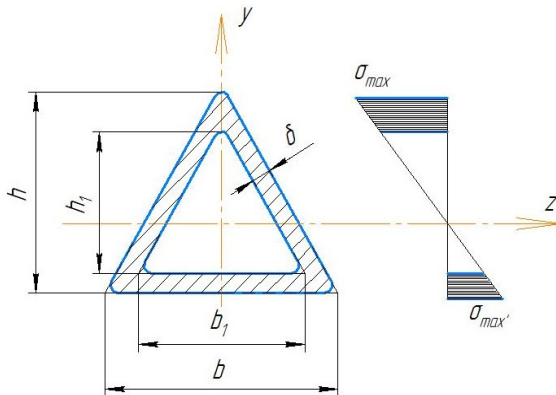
Эскиз треугольного сечения с эпюрой напряжений
